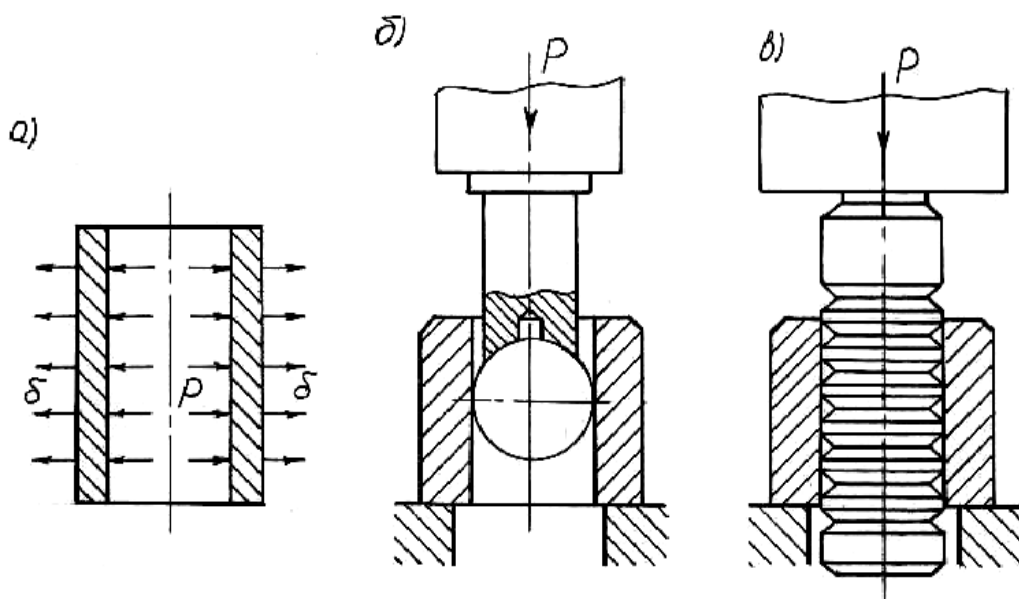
Раздача а) схема обработки; б) шариком; в) цилиндрической оправкой
